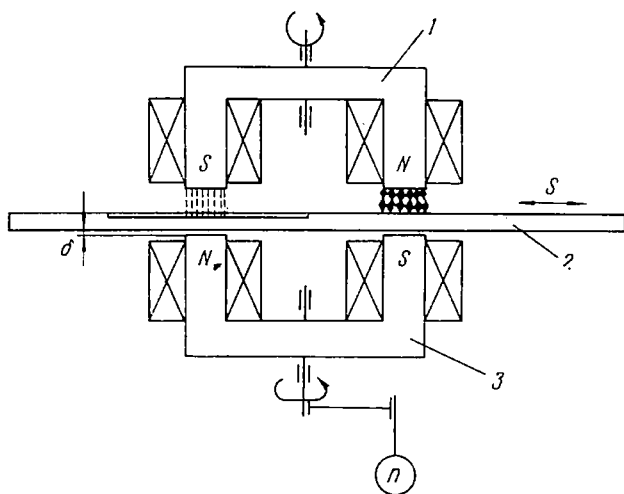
Схема установки для обработки крупногабаритных листов
